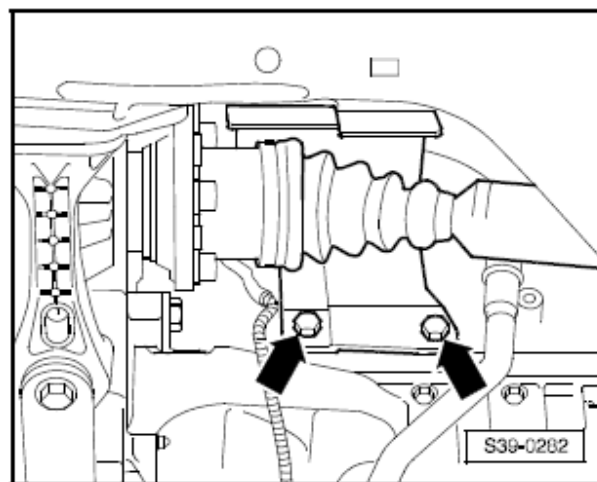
Розташування захисного ковпака карданного валу
